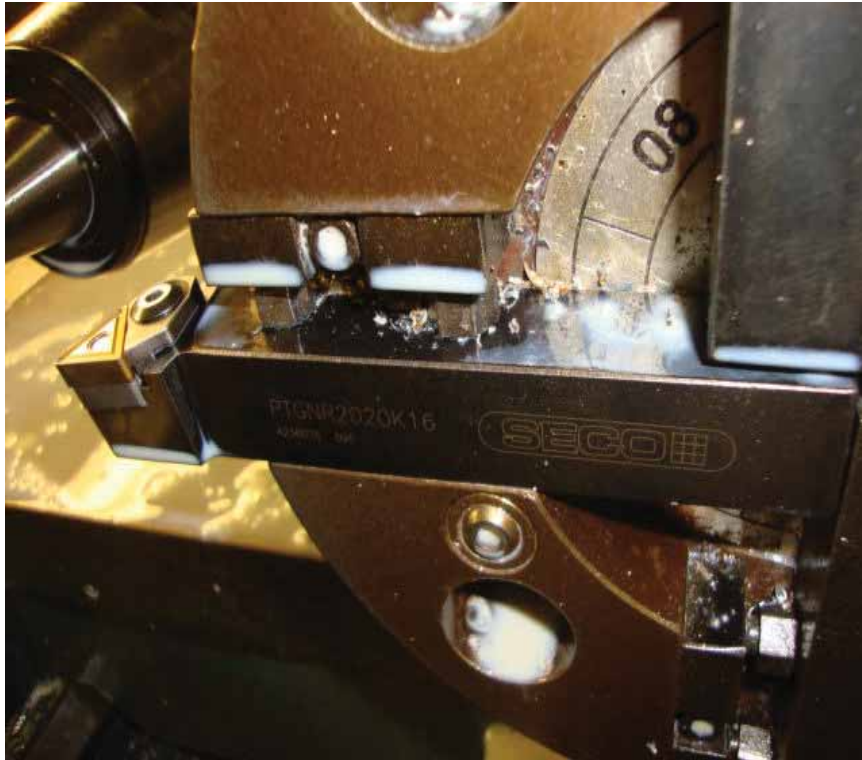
Suporte para inserto – Fabricante Seco Tools.
